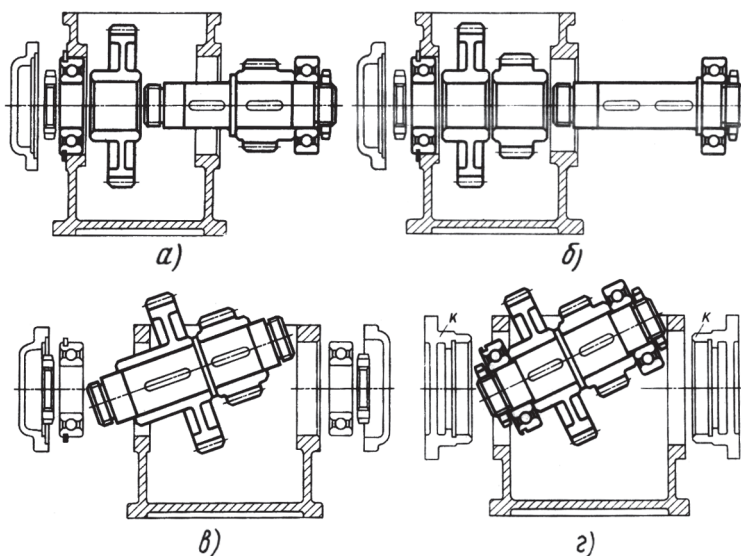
Влияние на конструкцию корпуса варианта сборки валов
